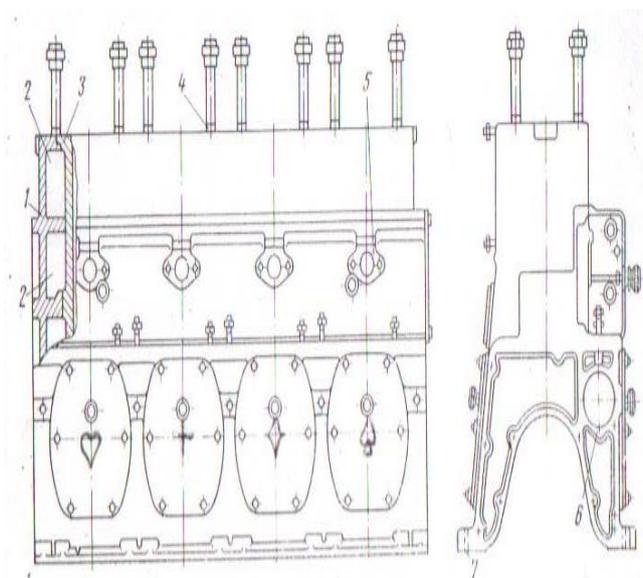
Блок цилиндров дизеля 4ДВ-224
